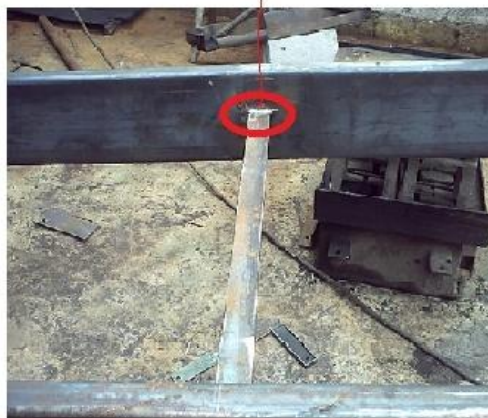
Proceso de Soldadura del Soporte de los Rodillos
